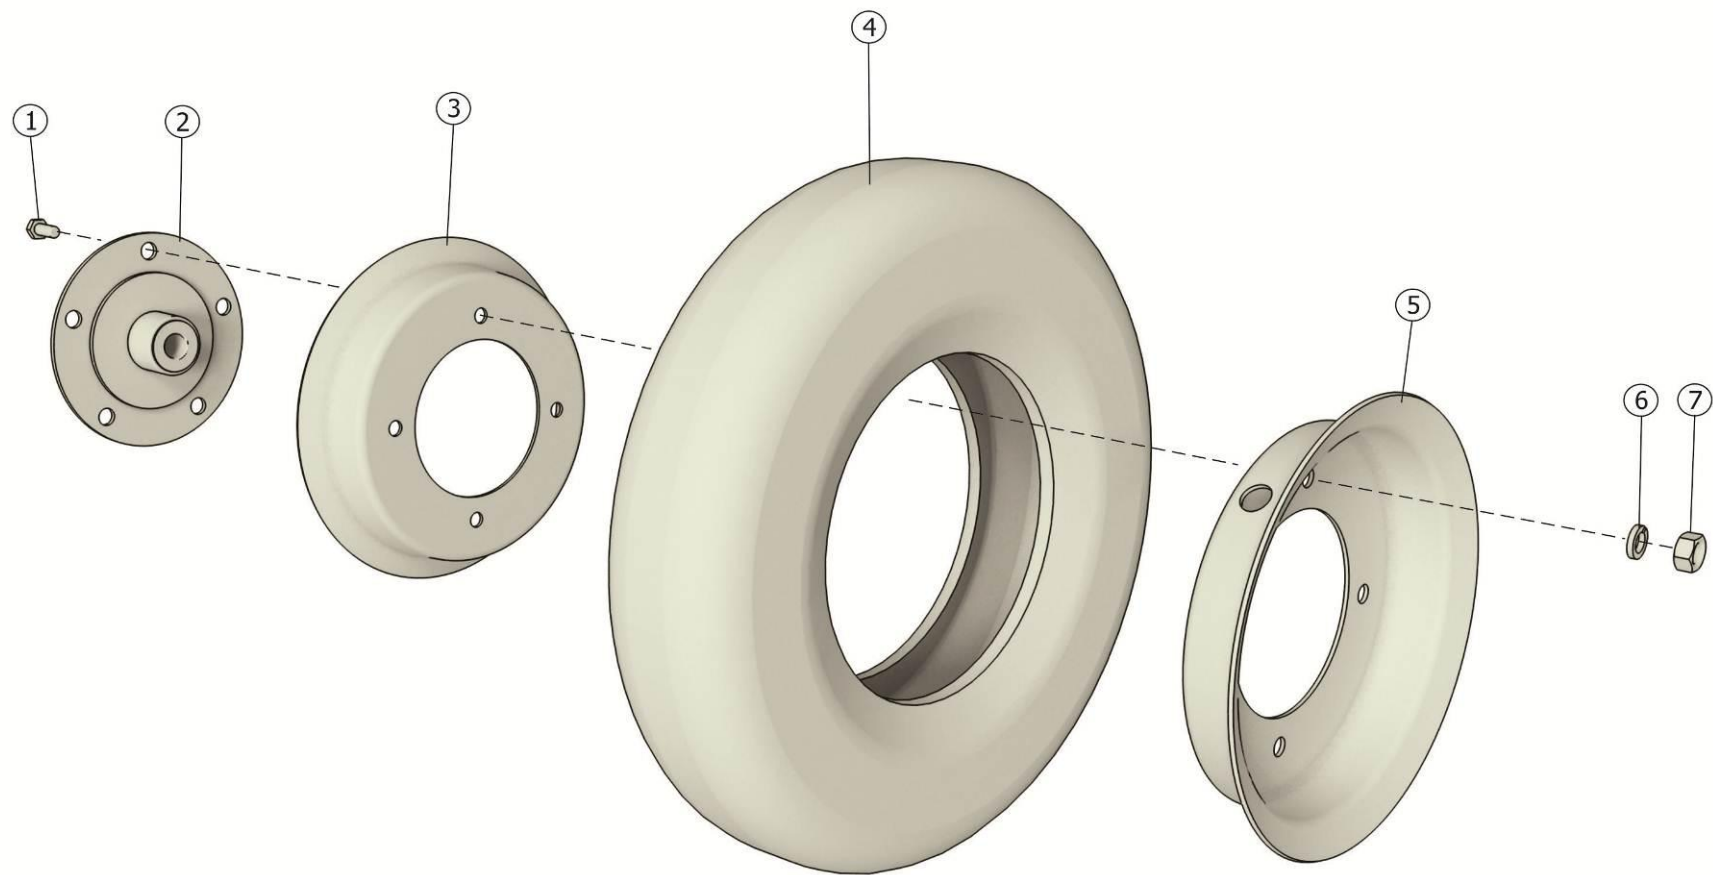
Колесо в сборе МЗС-90.01.100
